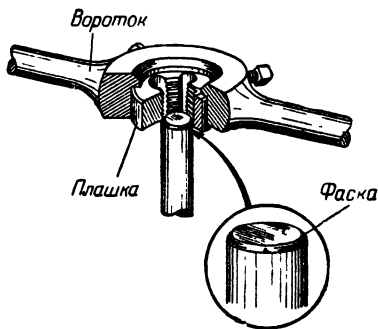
Ручная плашка для нарезания резьбы на болтах или винтах и вороток для вращения плашки.
